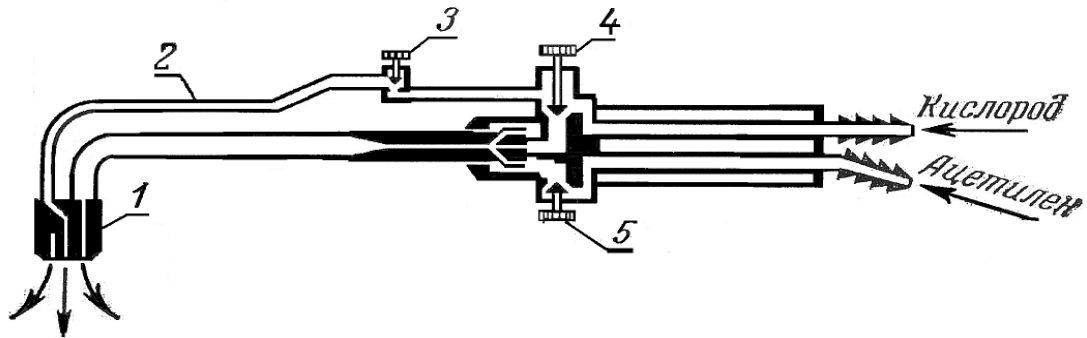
Схема устройства ручного резака инжекторного типа:
